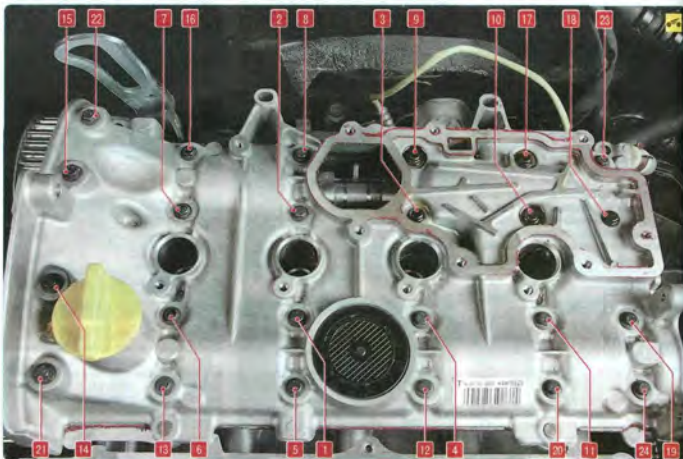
Порядок затяжки болтов крепления крышки головки блока цилиндров
